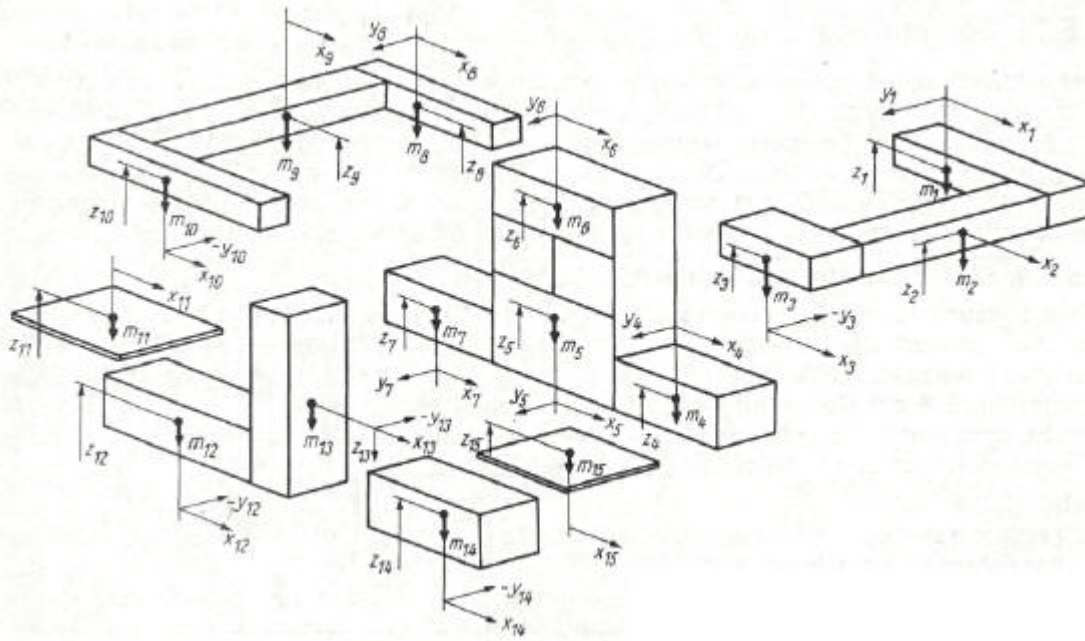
Belastungsschema der Einbauten einschließlich Zubehör und Zuladung
